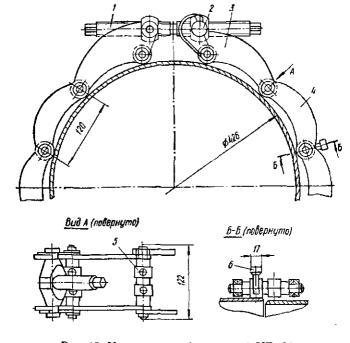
Центратор трубосварочный ЦТ-426: 1 — винт; 2 — гайка; 3 — шека; 4 — звено; 5 — ролих; 6 — рихтовочные винты
